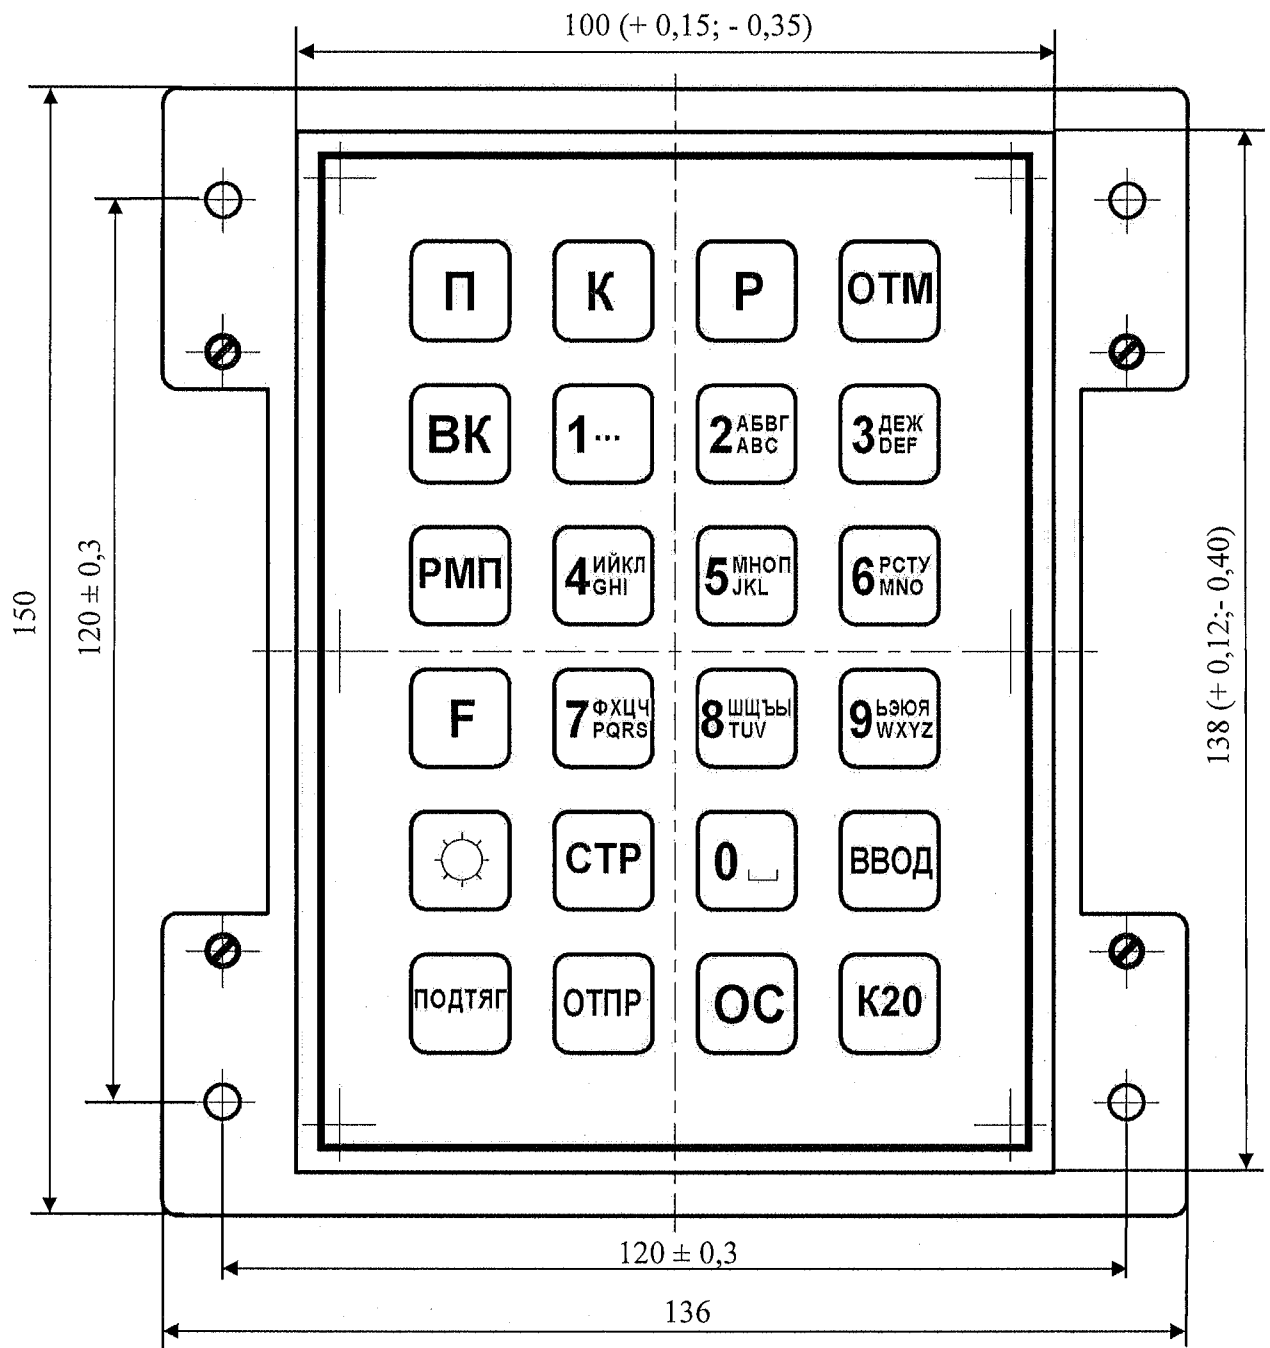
Внешний вид лицевой панели и присоединительные размеры модуля ввода 36905-250-00, модуля ввода М 36905-250-00-02
